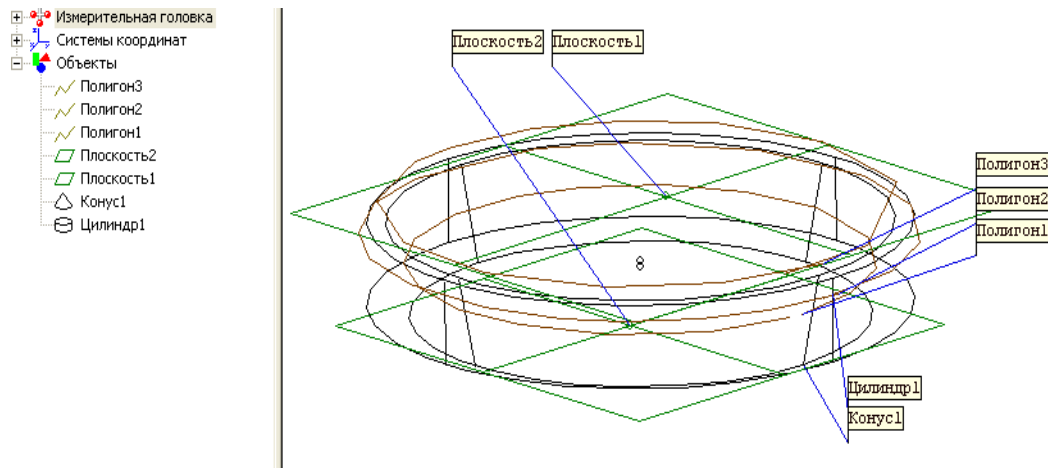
Сеанс вимірювання кільця роликового підшипника
